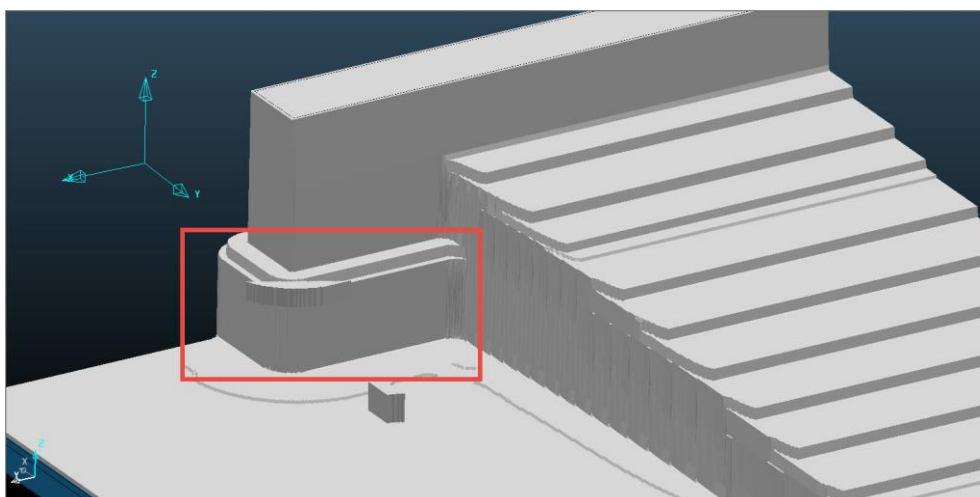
Simulação em ViewMILL para mostrar a zona que se teve que remover manualmente.
